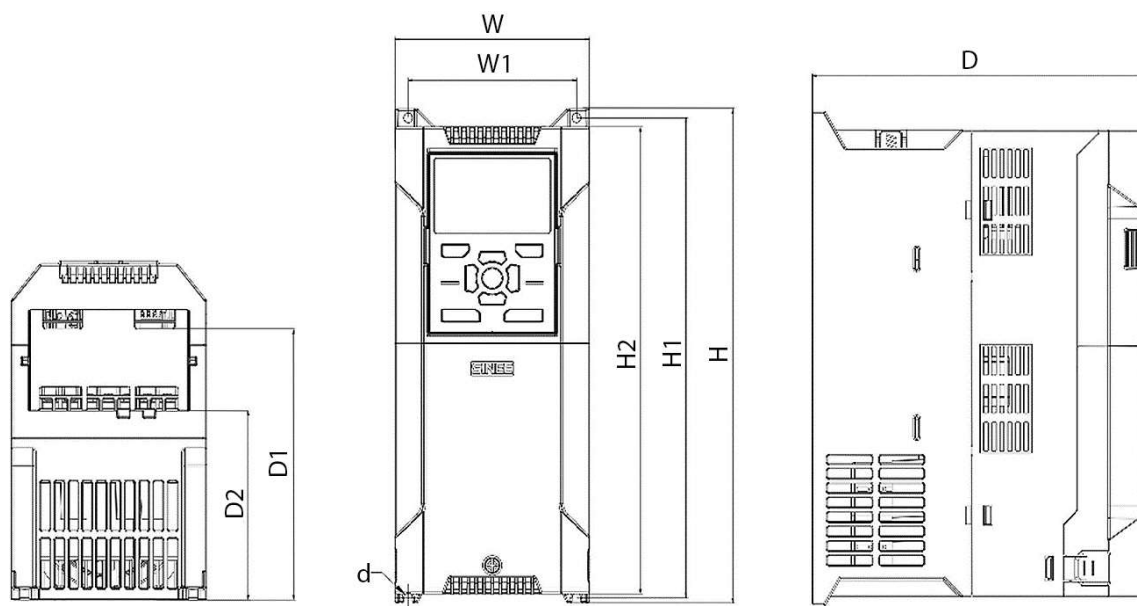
Внешний вид преобразователей E5-9600-001H...030H
